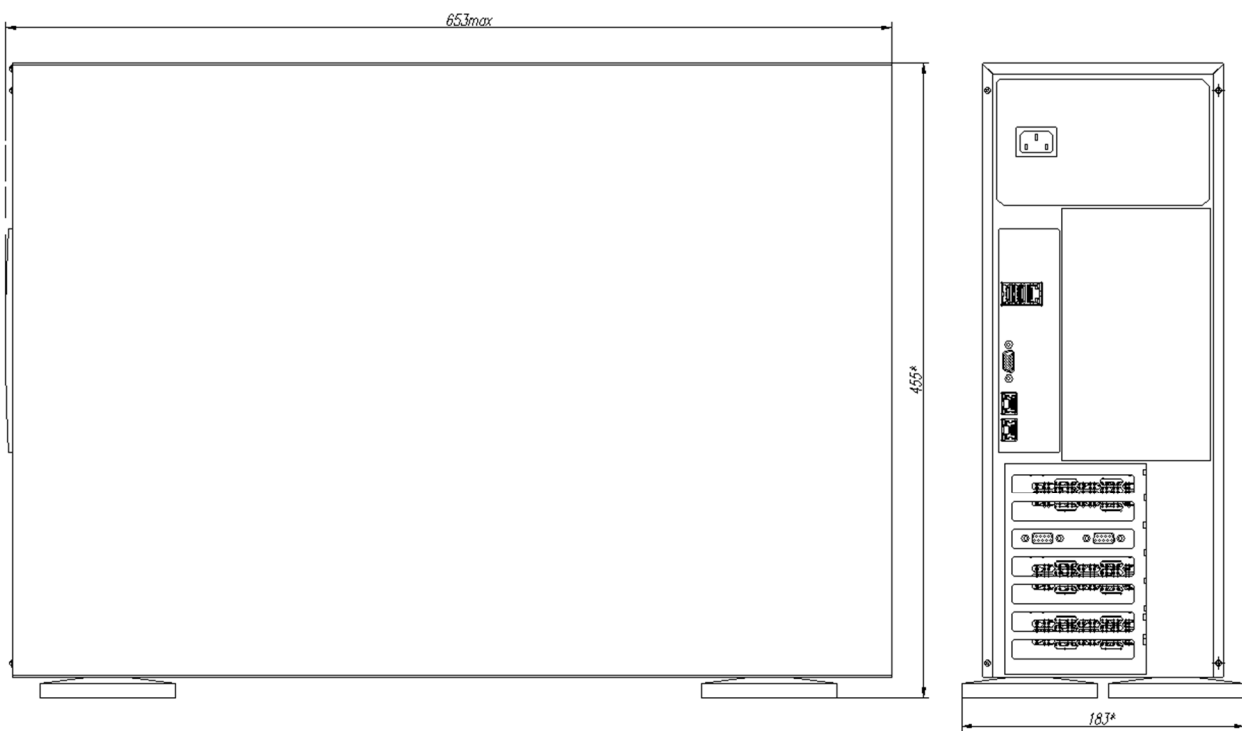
Габаритные размеры Блока в исполнении ЮФКВ.466531.005-02
